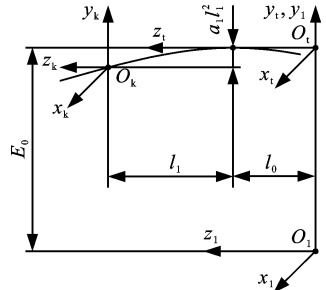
成形铣刀加工圆柱齿轮双向修形齿面的坐标系
